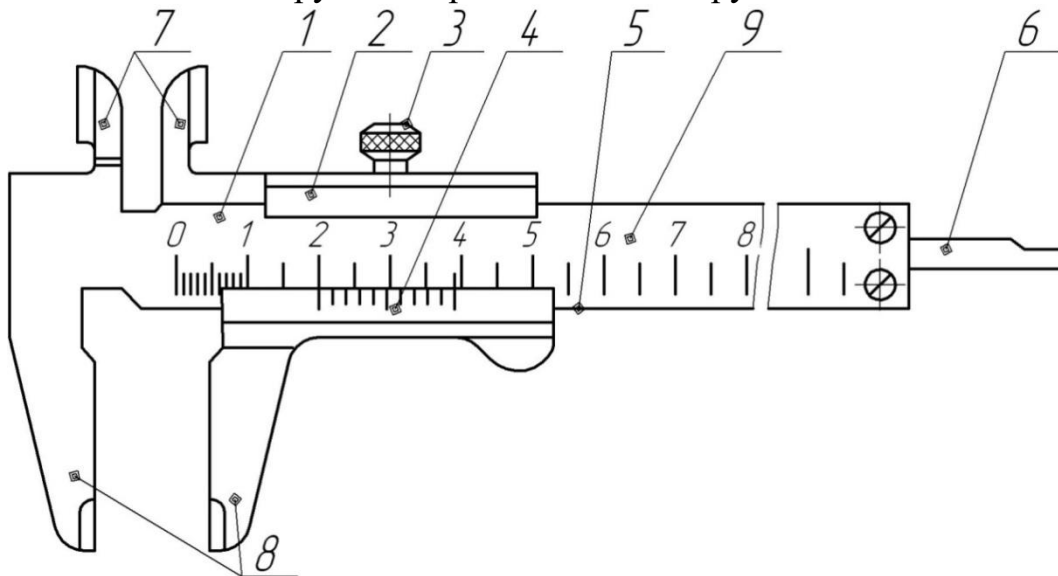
Конструкція та будова штангенциркуля ШЦ-I: 1 – штанга; 2 – рамка; 3 – фіксатор; 4 – ноніус; 5 – робоча поверхня штанги; 6 – глибиномір; 7 – губки з вимірювальними поверхнями кромek для вимірювання внутрішніх розмірів; 8 – губки з плоскими вимірювальними поверхнями для вимірювання зовнішніх розмірів; 9 – шкала штанги
